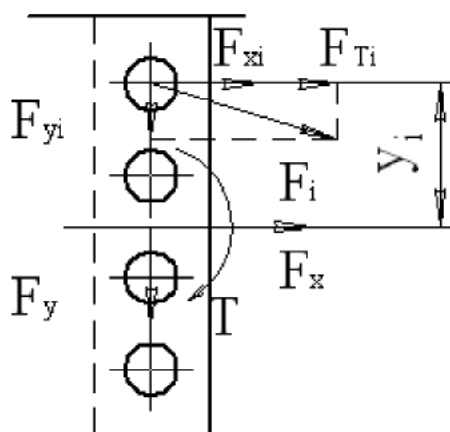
Схема нагрузок однорядного заклепочного шва
